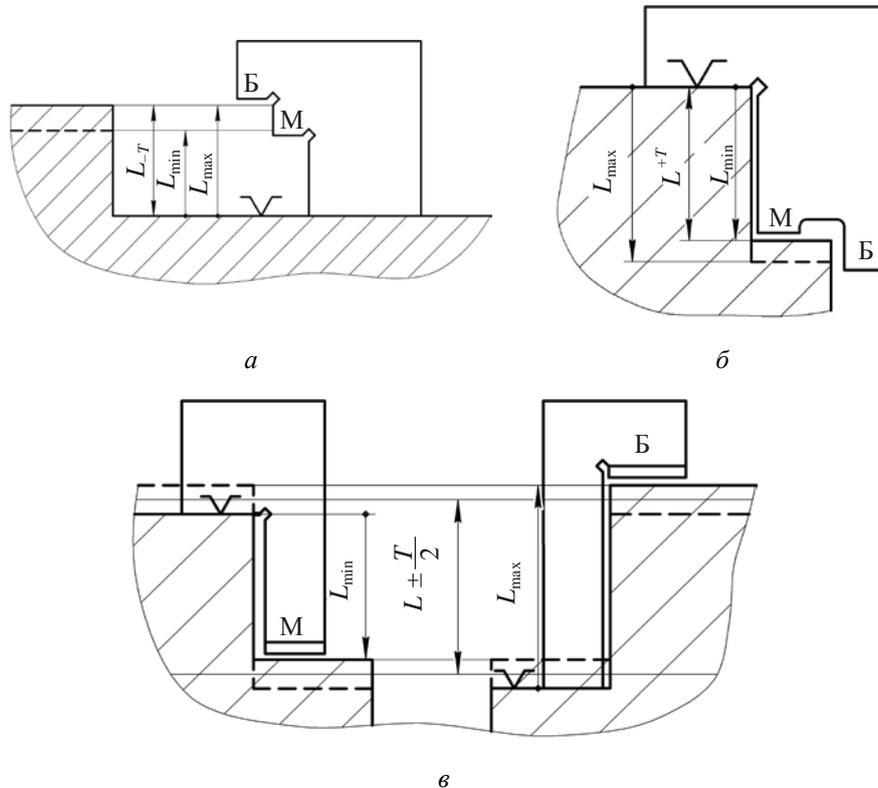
К выбору схем расположения полей допусков калибров:
